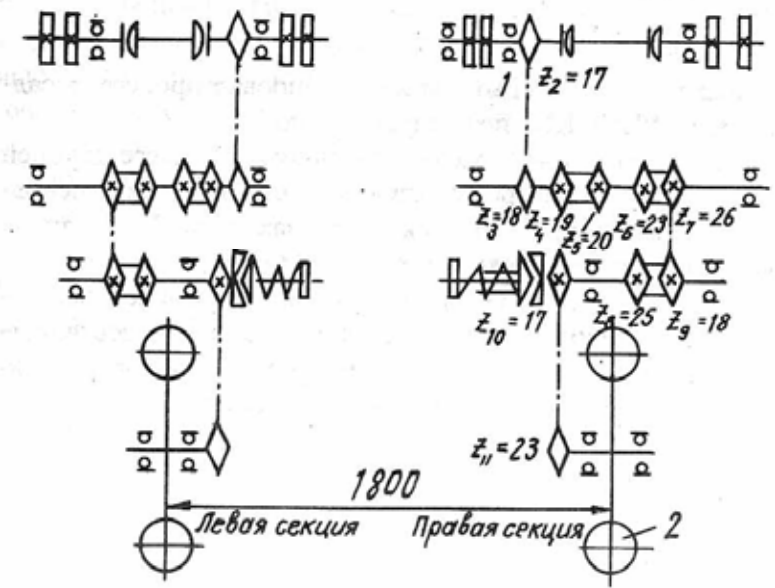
Схема кинематическая привода сажалки: 1-посадочные аппараты; 2-опорно-приводное колесо
